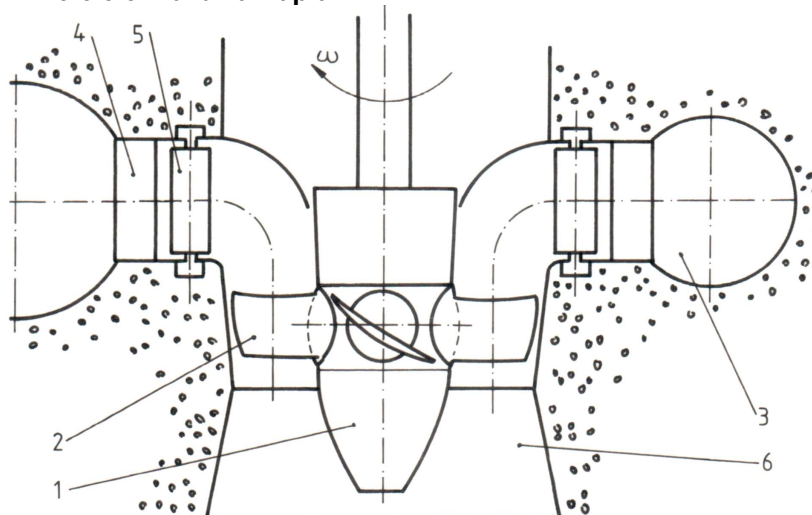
Turbina Kaplan: 1 - rotor; 2 - palete rotorice; 3 - cameră spirală; 4 - palete statorice fixe; 5 - palete statorice reglabile; 6 - aspirator
